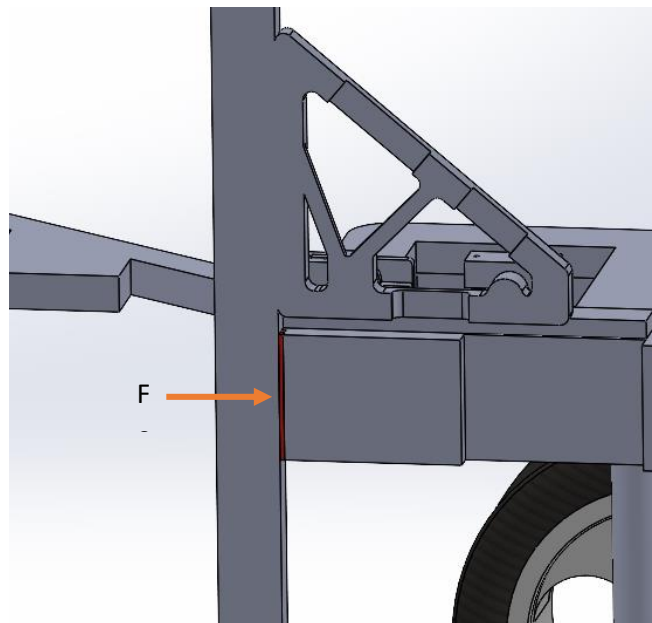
Punt de recolzament de la columna a la base (Font pròpia)
